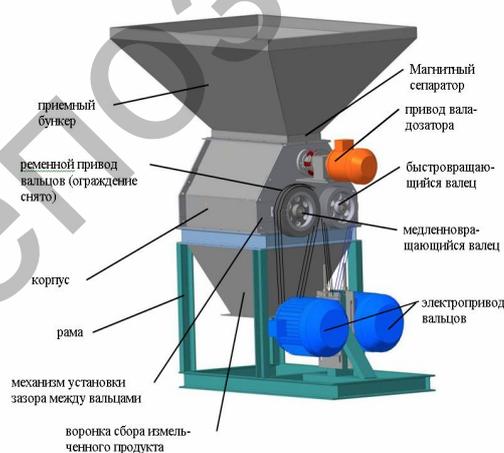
Схема конструкции и общий вид разработанной вальцовой дробилки зернофуража
